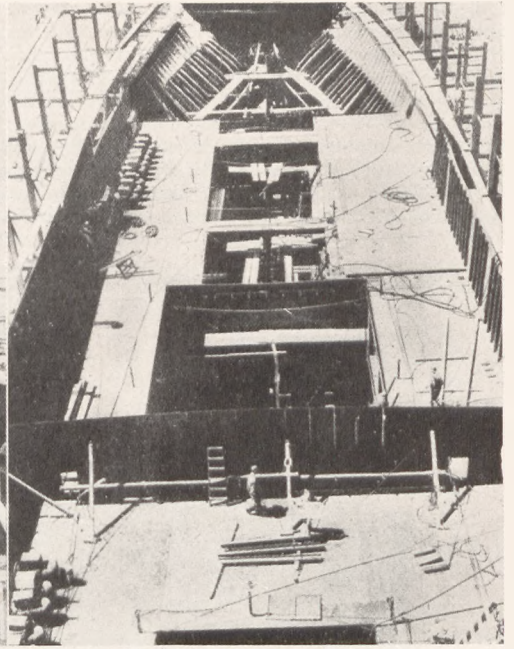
Einlegen des Zwischendecks aus zusammenschweißten größeren Plattenstücken.
